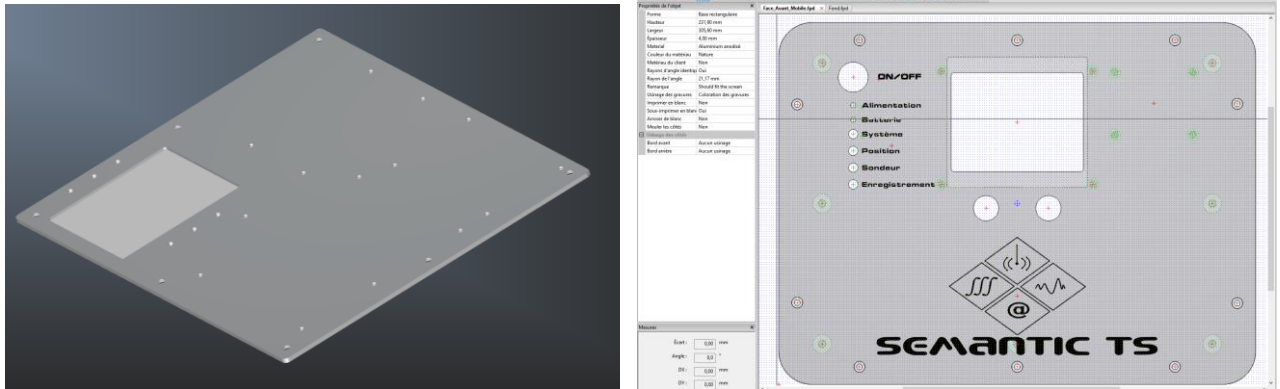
Conception du bloc de fixation (fond et façade) par CAO
